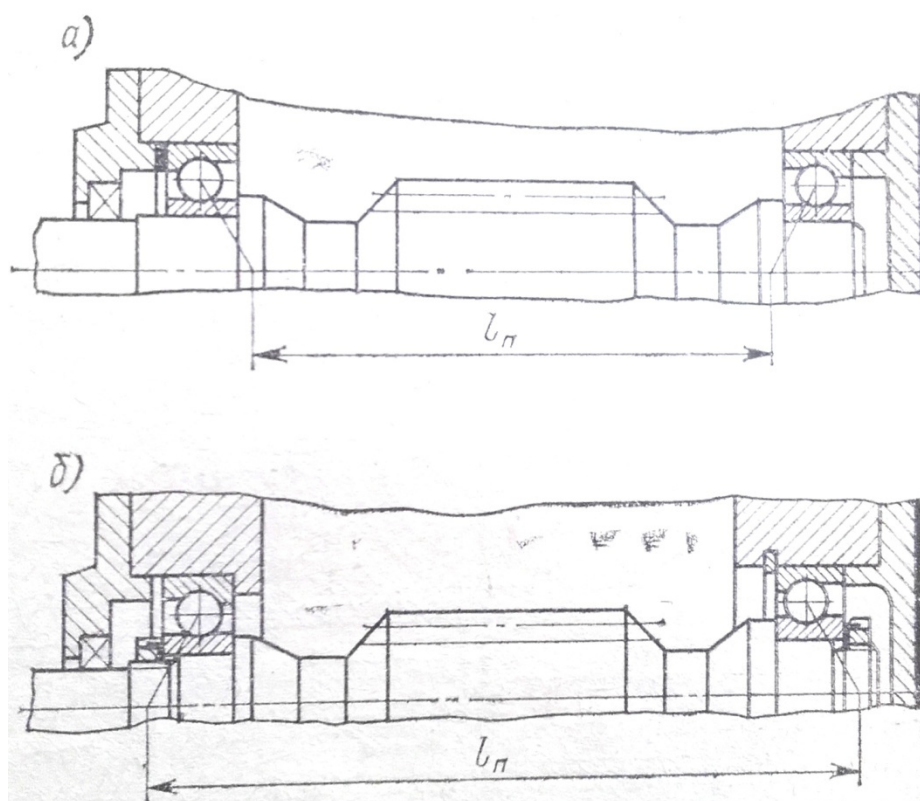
Опоры червяка с радиально-упорными шарикоподшипниками, установленными: а – враспор; б – наружными кольцами внутрь
